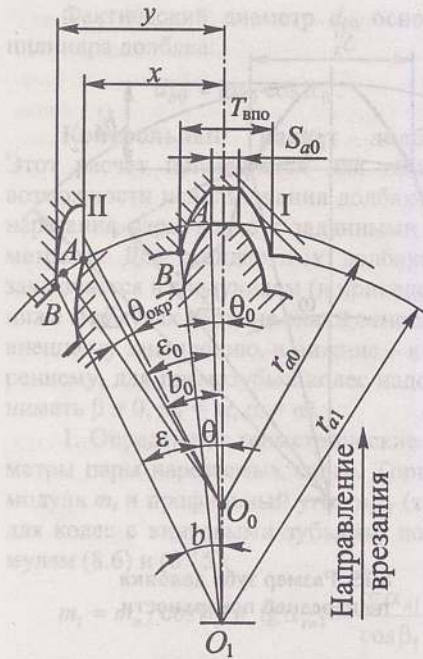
Схема проверки долбяка при нарезании колеса с внутренними зубьями
